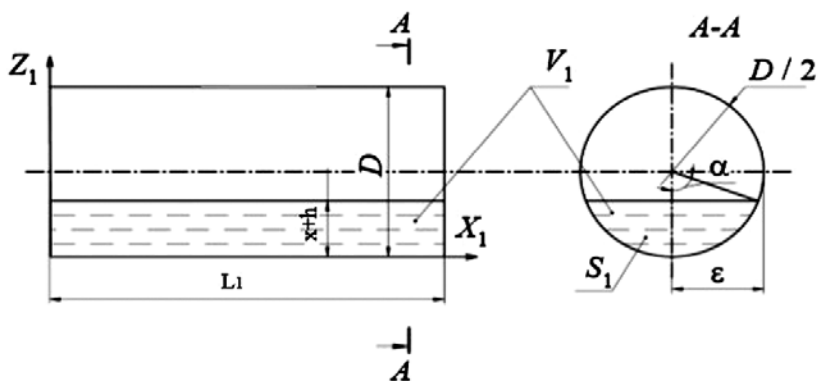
Чертеж цилиндрической и эллиптической частей цистерны
